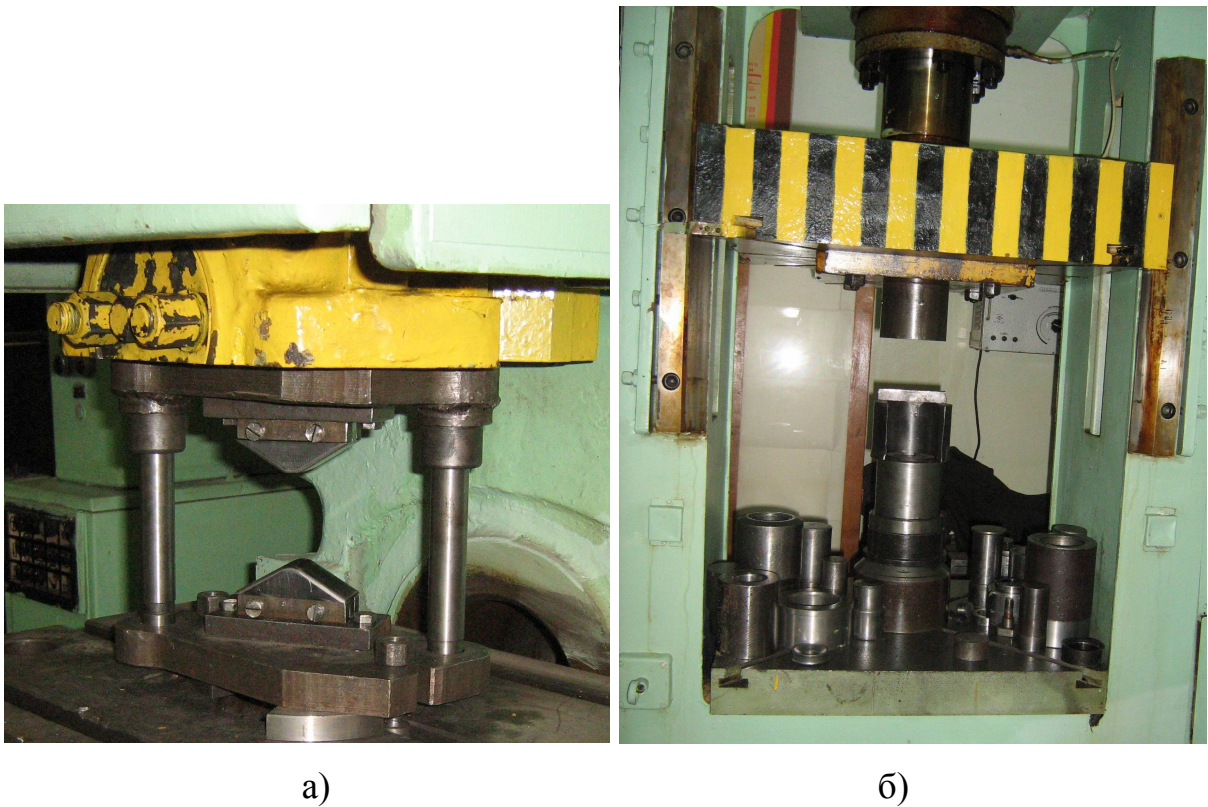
Фото оборудования и оснастки для профилирования (а) и осадки заготовок (б)
